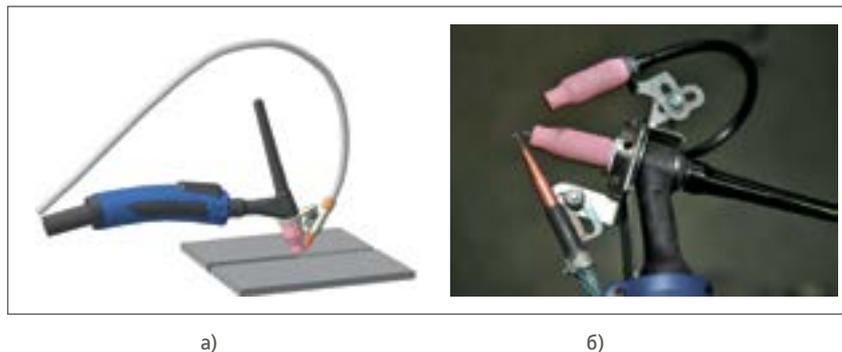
Внешний вид аргодуговой горелки для механизированной подачи сварочной проволоки сплошного сечения:
